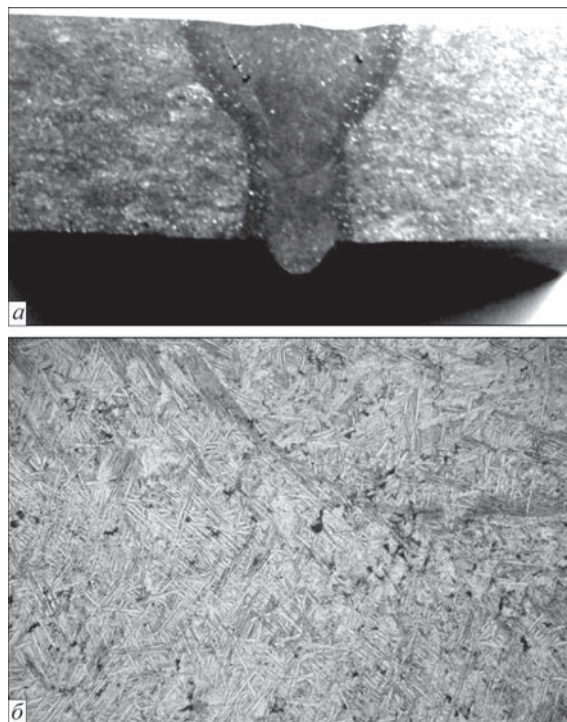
Структура образца № 2: а — поперечный макрошлиф сварного соединения; б — структура ЗТВ ($\times 200$)
